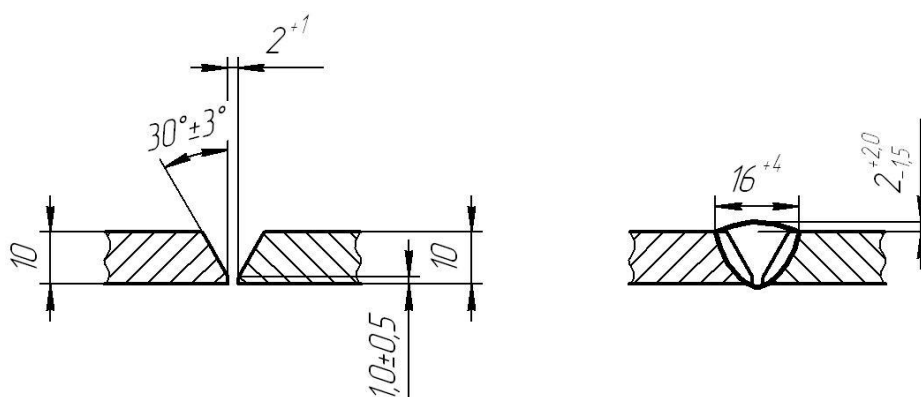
Подготовка кромок, сборка стыка и геометрия сварного шва
